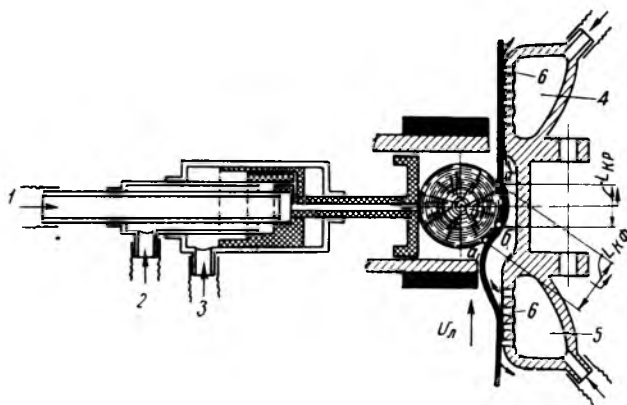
Схема многоступенчатого пневматического цилиндра с отбором воздуха для обдувки и подпора абразивной ленты (воздушная смазка):
